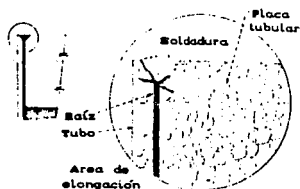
Grietas propagándose en la soldadura, tubo y placa tubular
